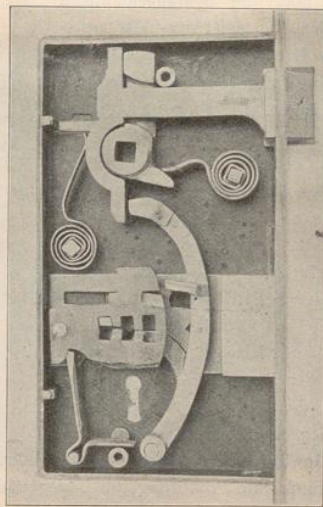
Eingestecktes Chubb'sches Schlofs mit vier Zuhaltungen und mit sicherer Tagesfalle.
